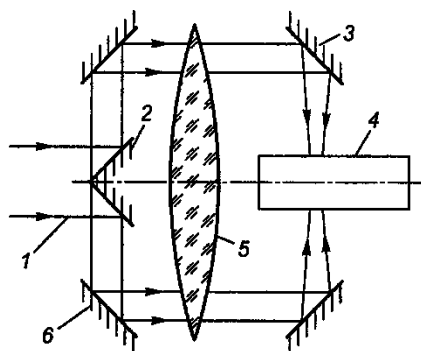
Система для обработки цилиндрических поверхностей деталей
